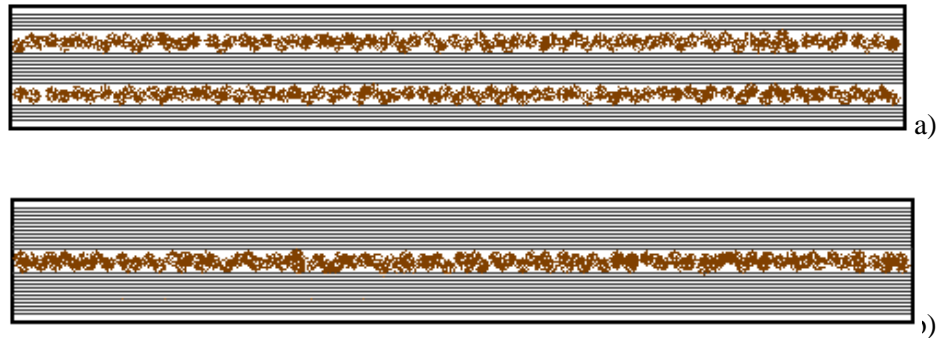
Tipos de empilhamento usados nas amostras para ensaios estáticos. a) empilhamento A, b) empilhamento B.
